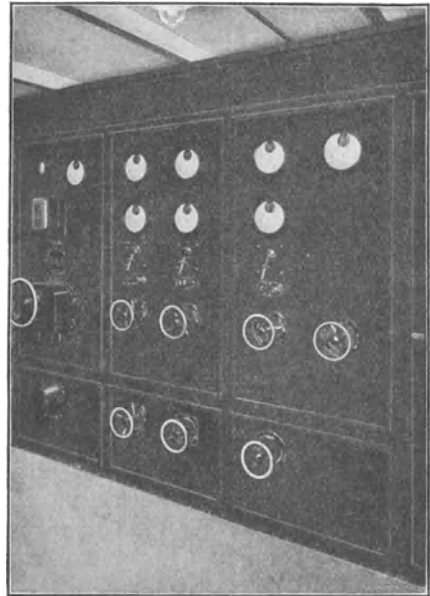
Schalttafel für einen Mehrphasenschweißumformer.
